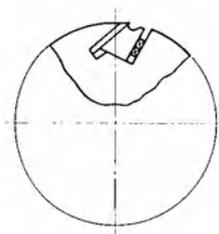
Druckschraubenbefestigung für Hobelmesser.
